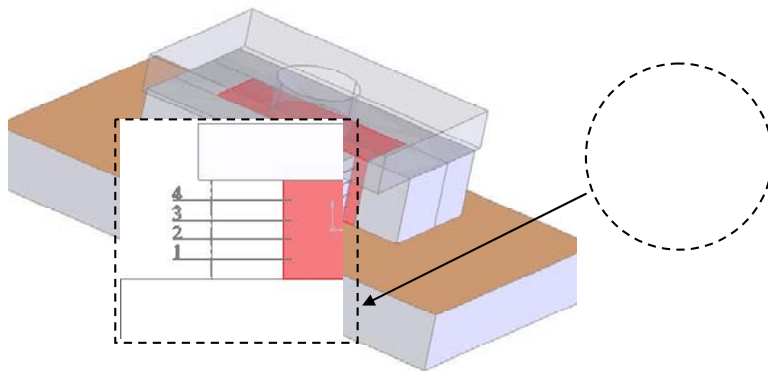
Схема размещения термопар в боковой стенке кокиля в качестве датчиков заливки слоев
